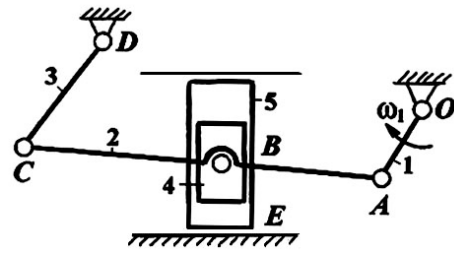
Механизм пресс-автомата с плавающим ползуном
